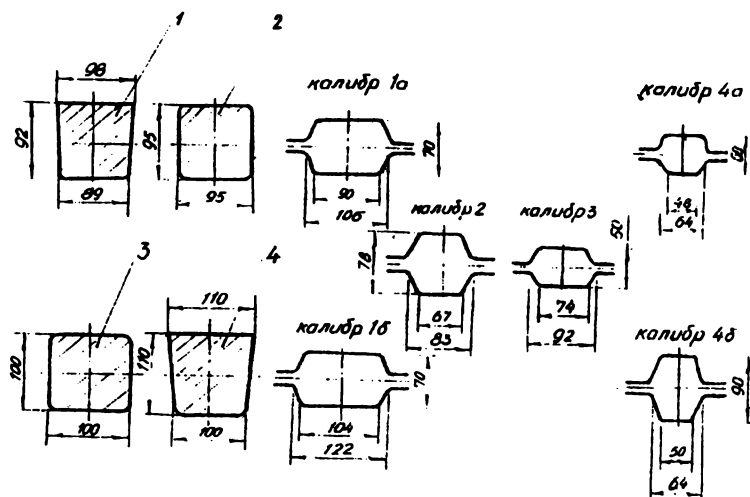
Типоразмеры поперечного сечения исходных слитков и схема калибровки ОК 500: 1,4 - медные слитки горизонтальной отливки вида СН-М1 массой 85 и 120 кг (ГОСТ 193-79); 2 - прессованная заготовка из кадмиевой бронзы; 3 - медный слиток вертикальной непрерывной отливки вида СВ-МО6 (ГОСТ 193-79)
